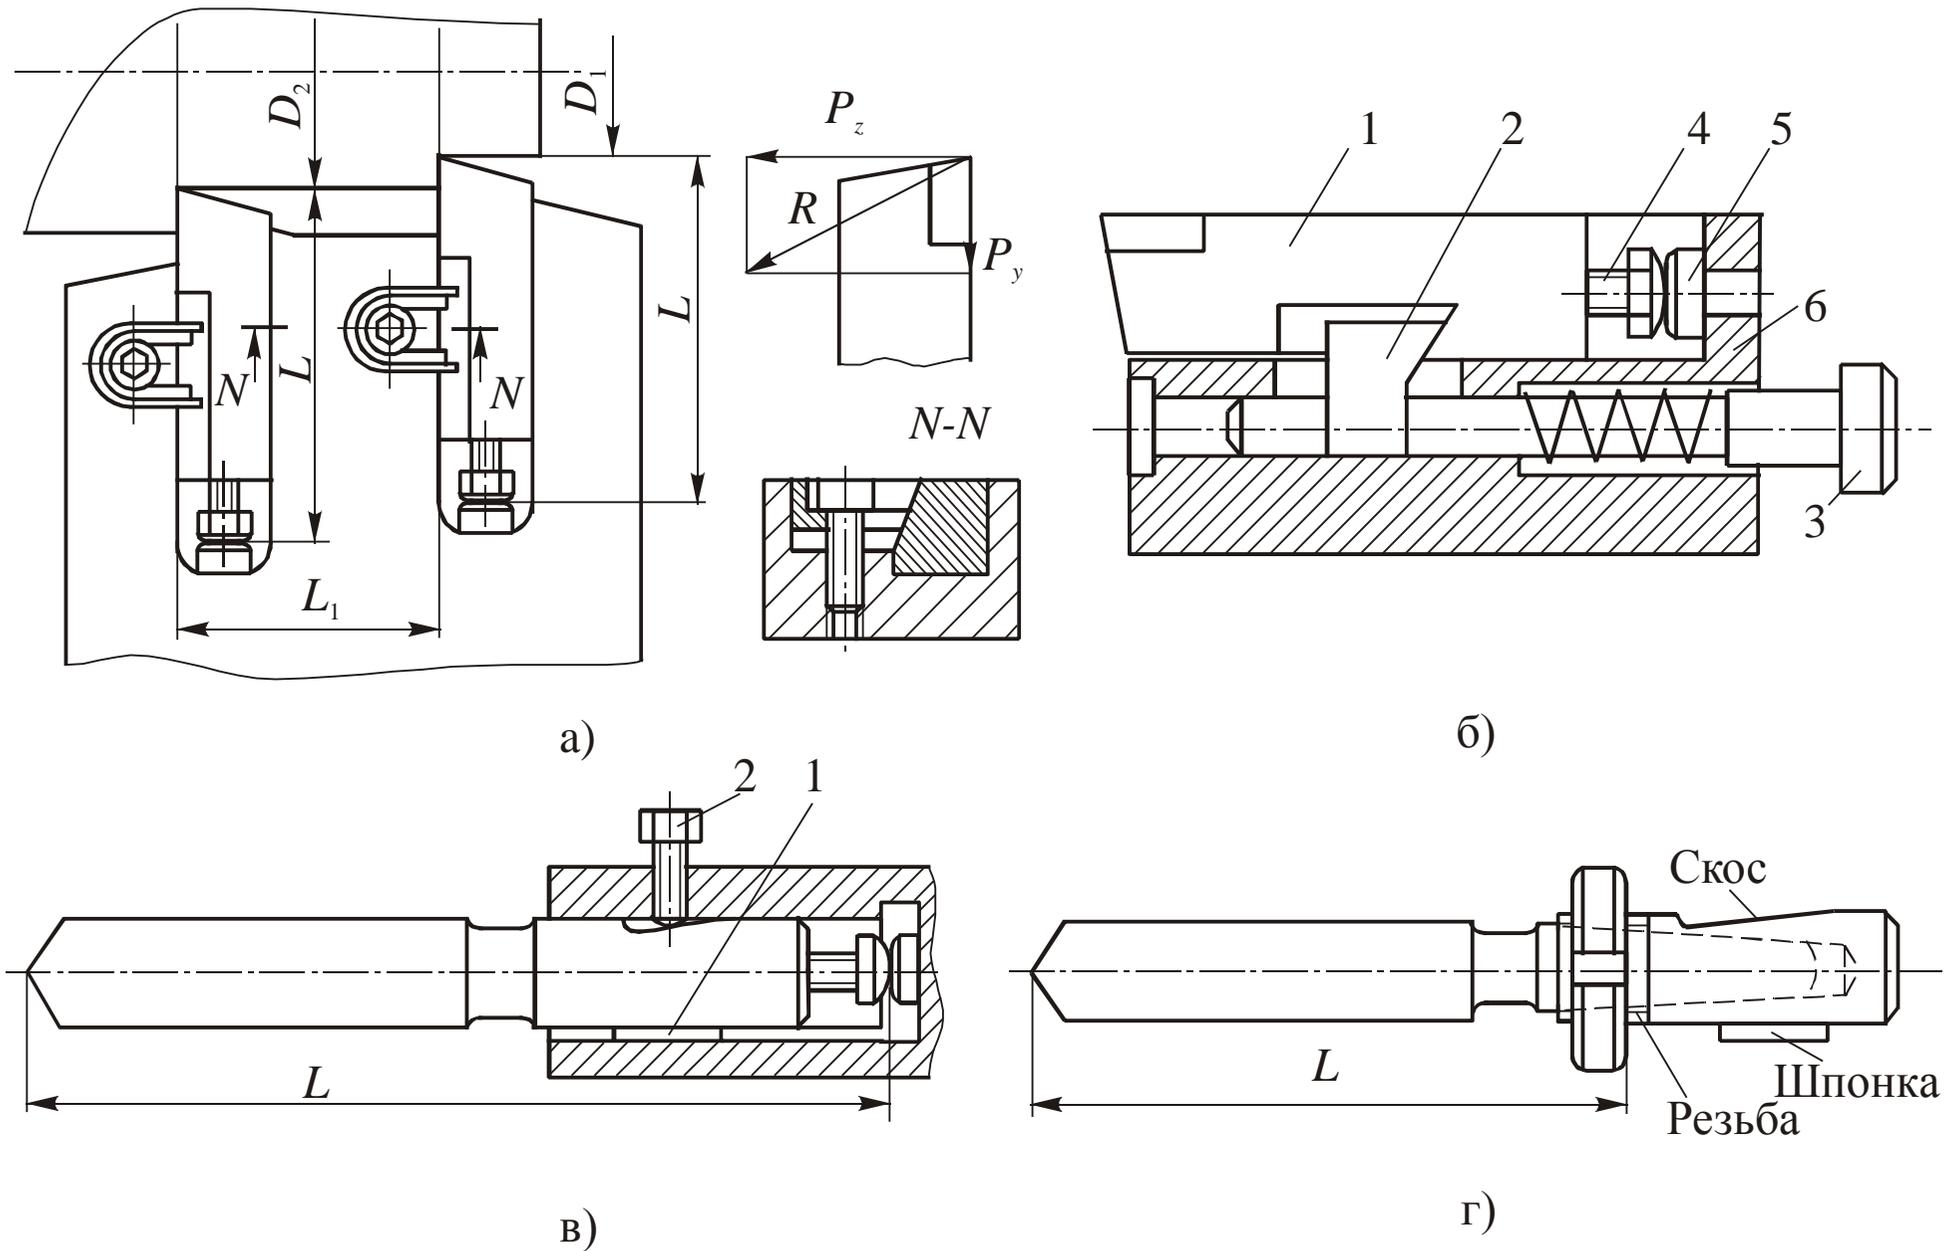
Устройства для бесподналадочной замены: а, б – резцов; в, г – осевых инструментов
